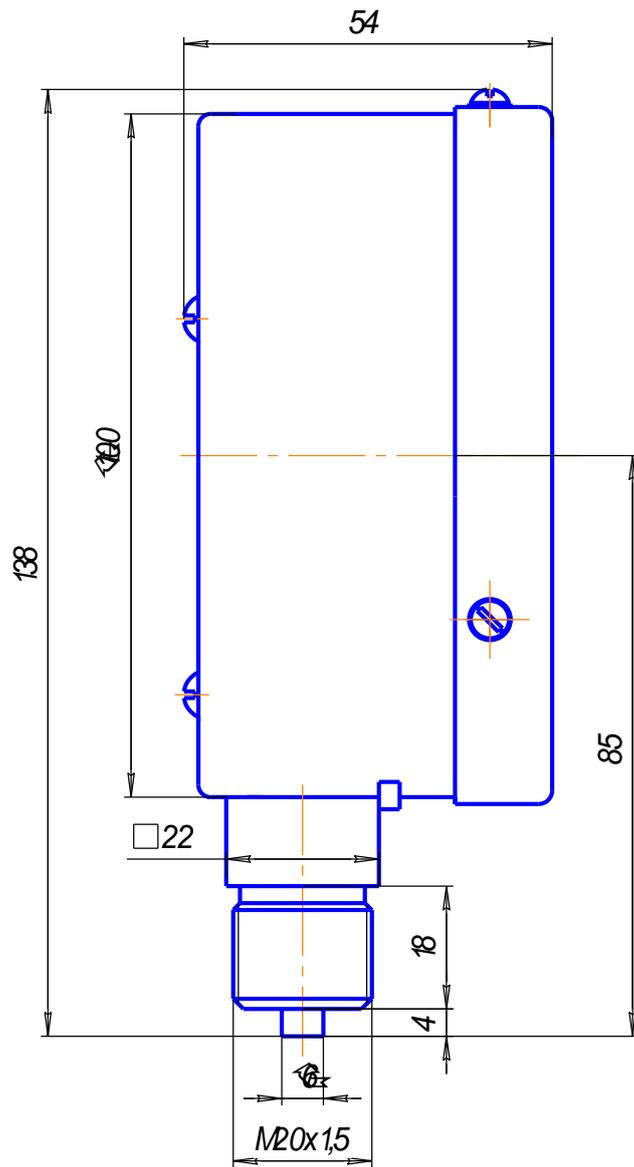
Габаритные и присоединительные размеры прибора с радиальным исполнением штуцера
